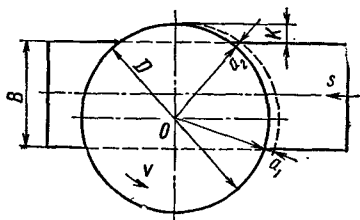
Схема смещения фрезы относительно заготовки при фрезеровании жаропрочных и нержавеющей сталей
